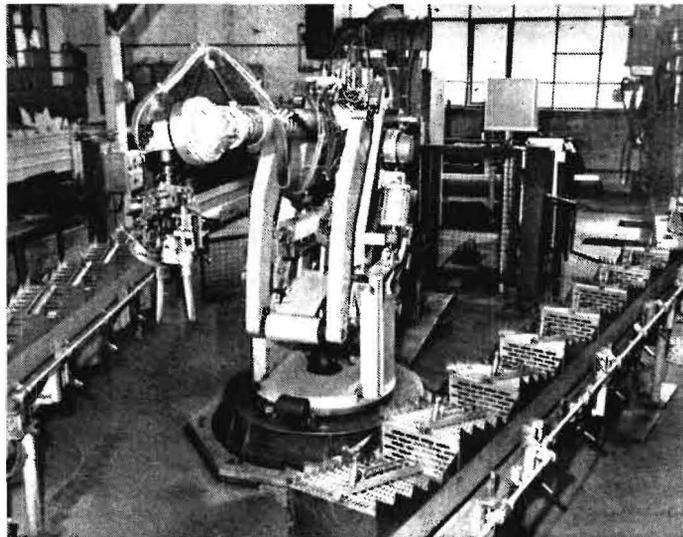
Hauptansicht der Roboter-Schweißanlage für Schüttler
